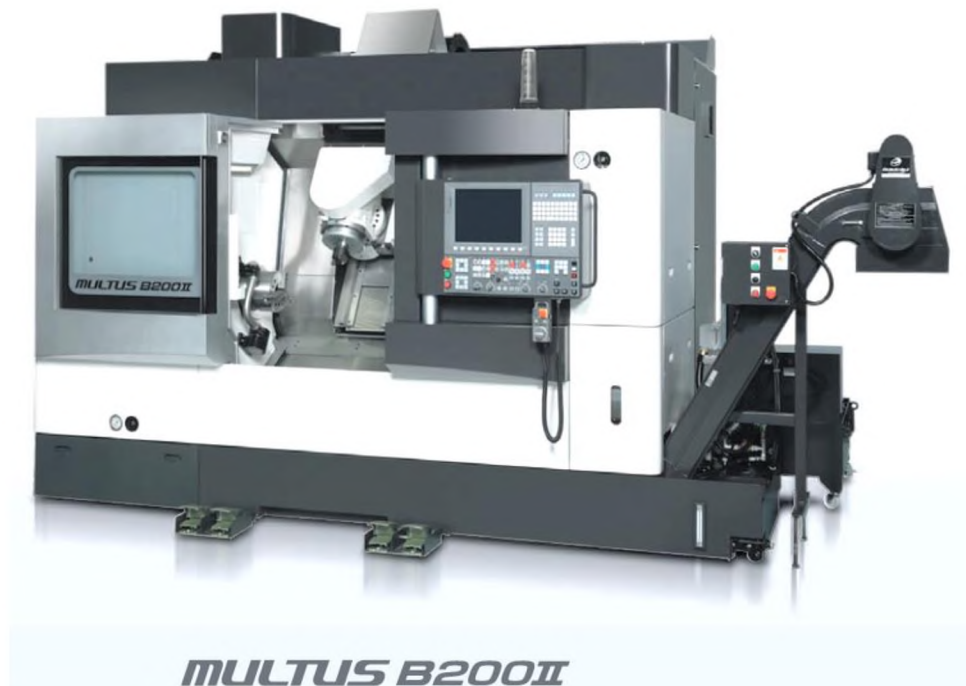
Токарно-фрезерний багатофункціональний верстат Okuma Multus B200II
